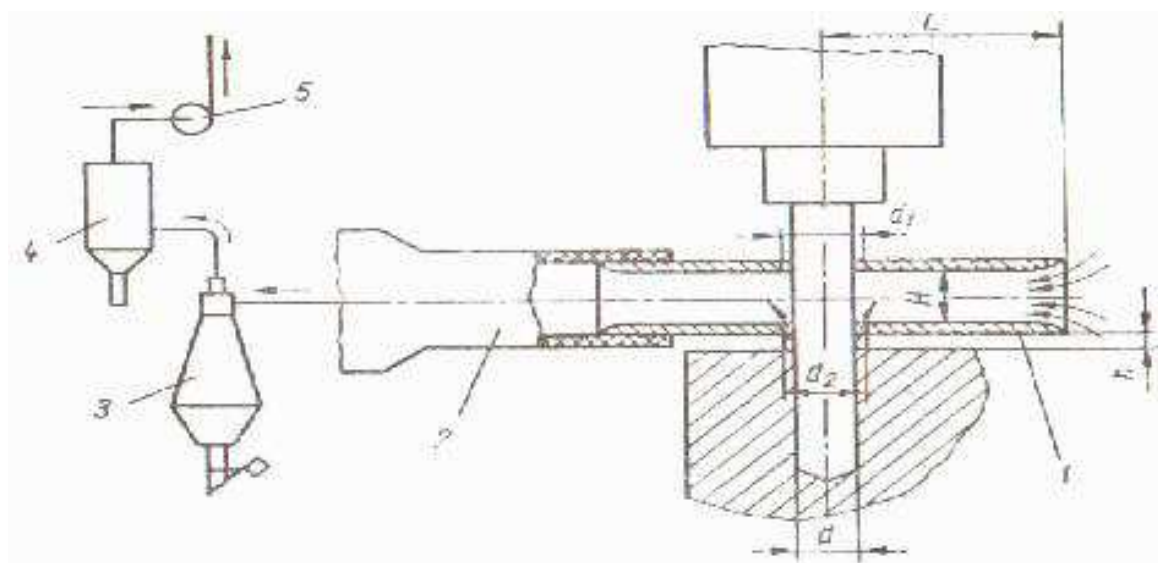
Пилостружкоприймач для свердлильного верстата:
